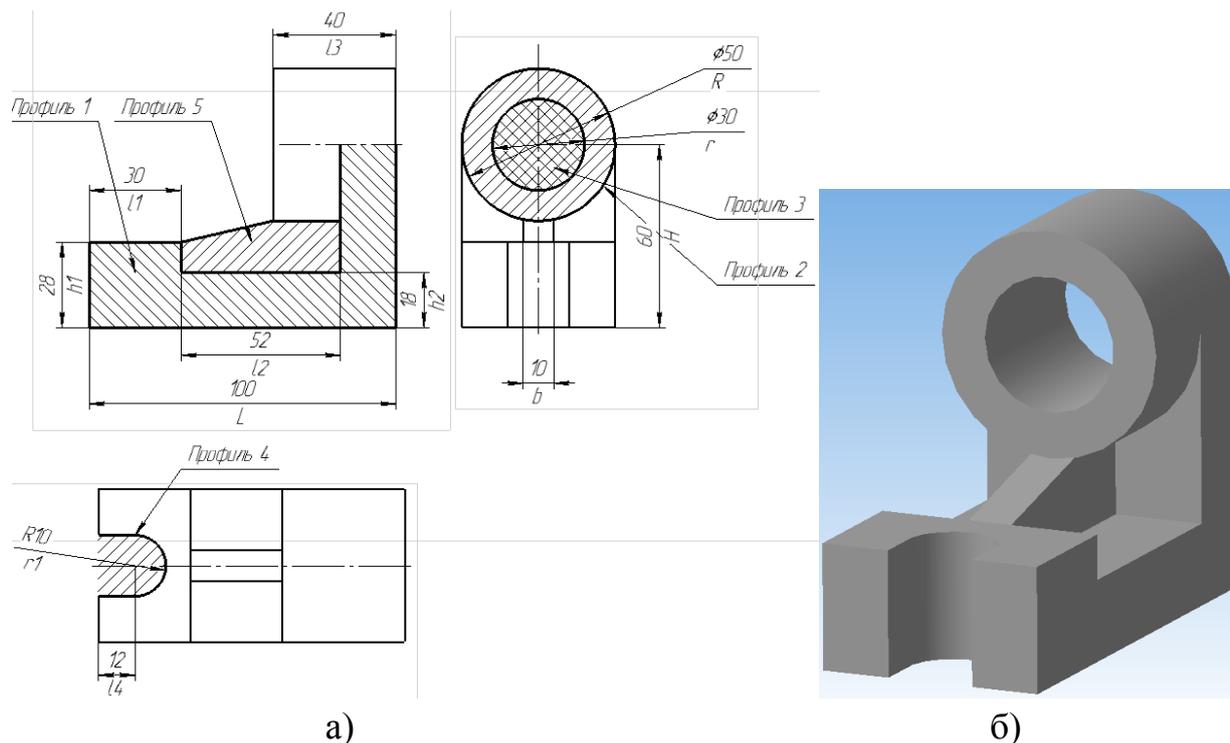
чертеж (а) и 3D модель (б)
